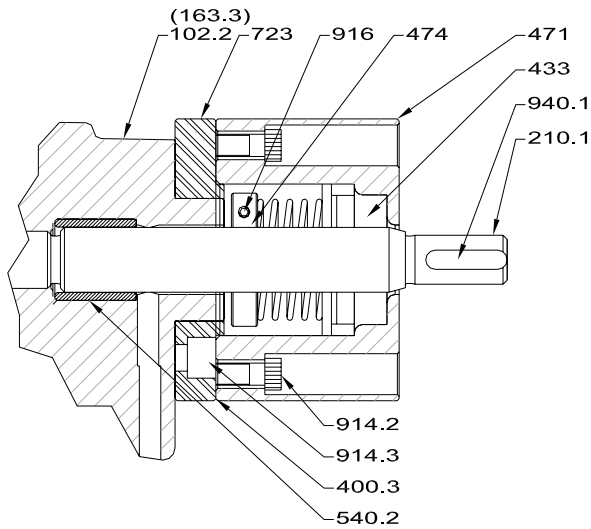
Desenho em Corte bomba FBE c/ selo mecânico
